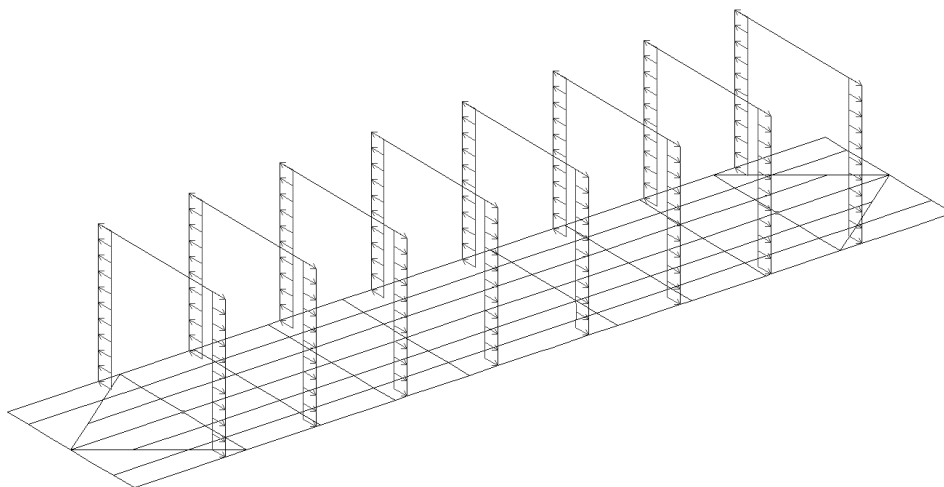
Розрахункова схема несучої конструкції вагона-платформи
